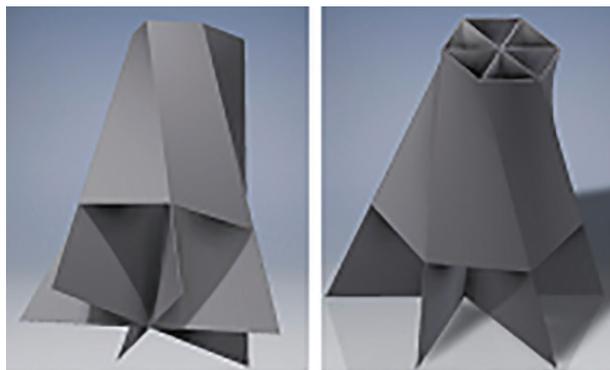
Внешний вид модели конфузорной конструкции с углом поворота верхней плоскости на 60° относительно центральной оси
